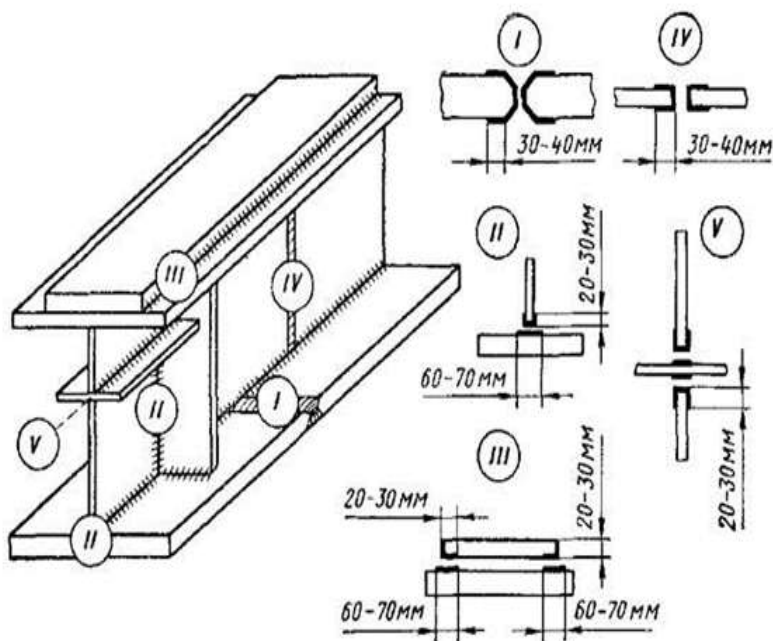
Участки металла, зачищаемые перед сваркой (указаны жирной линией)
